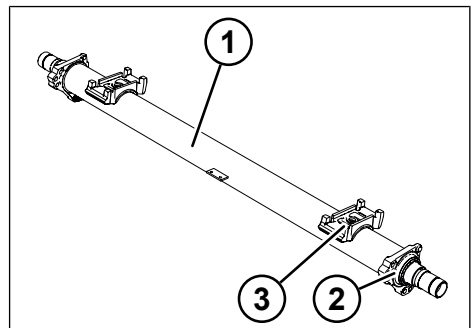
Bauteile des Achskörpers (Luftfederlenker oben)
